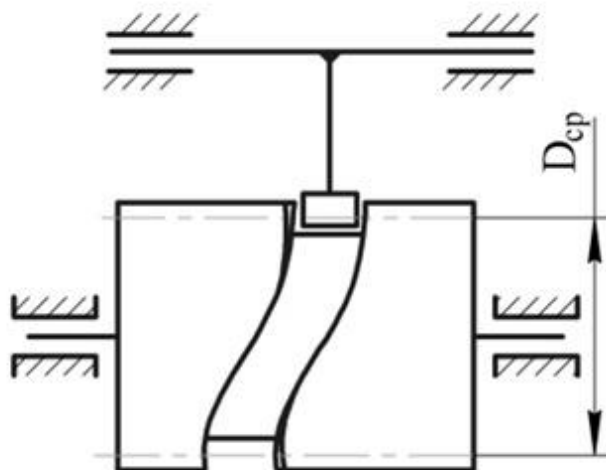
Цилиндрический кулачок с поступательно-движущимся толкателем
